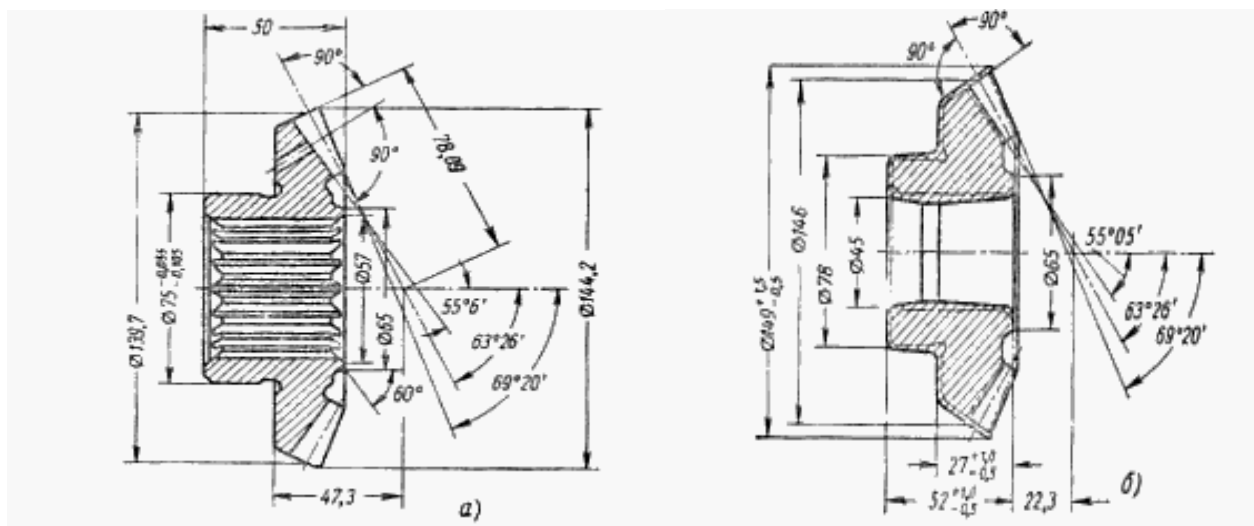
Чертежи детали (а) и поковки (б) шестерни полуоси
